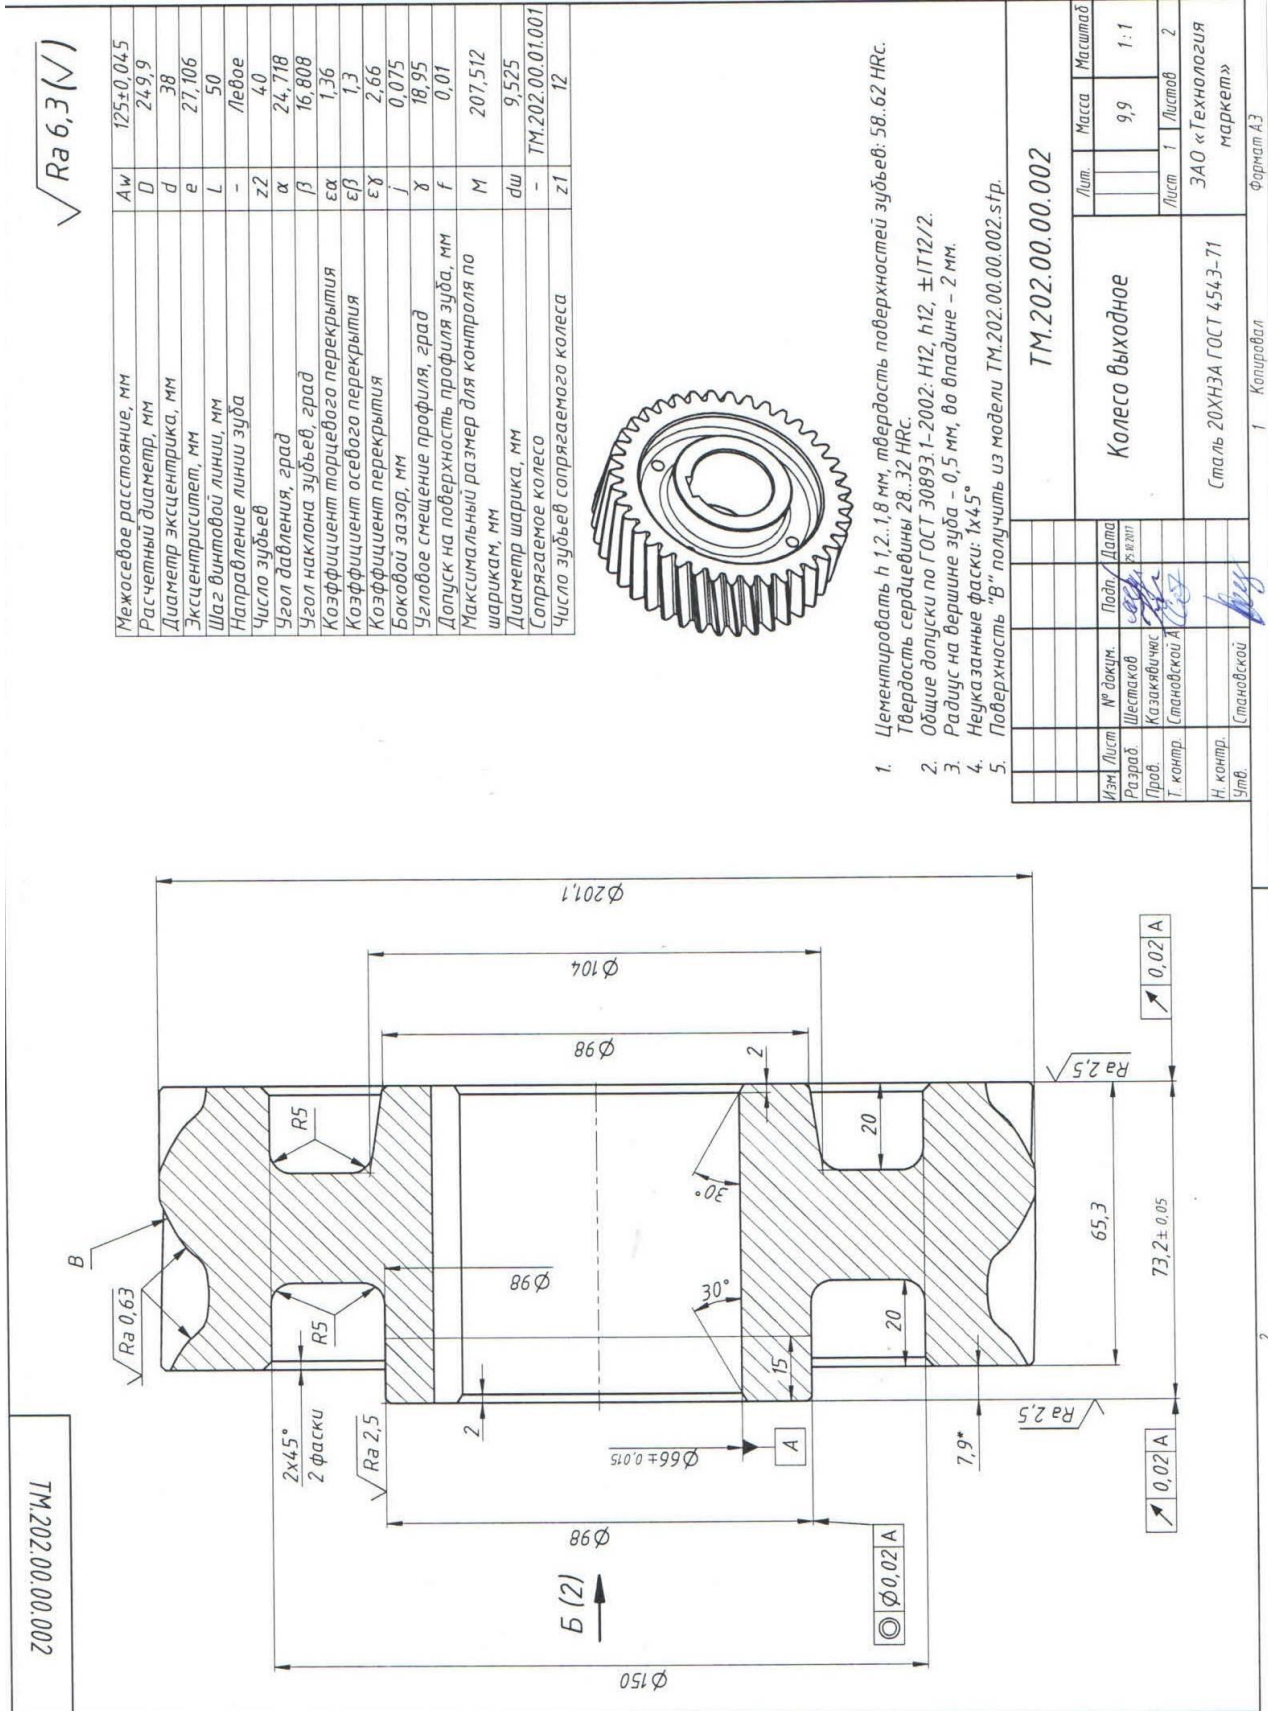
Чертеж колеса выходного редуктора с ЭЦ зубчатым зацеплением
